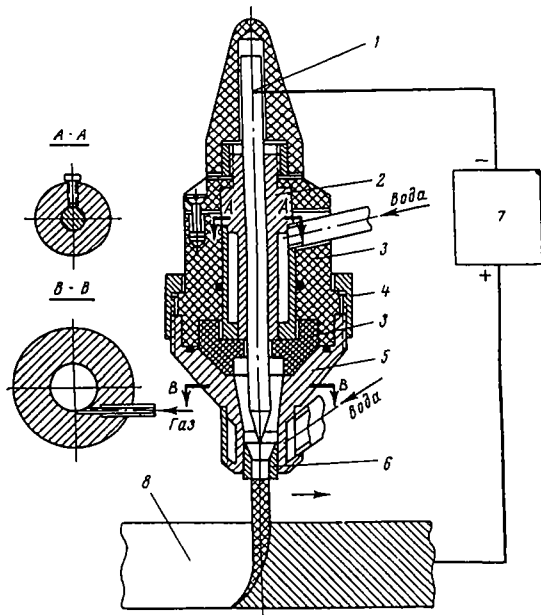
Общий вид плазмотрона и схема процесса плазменной резки металла:
